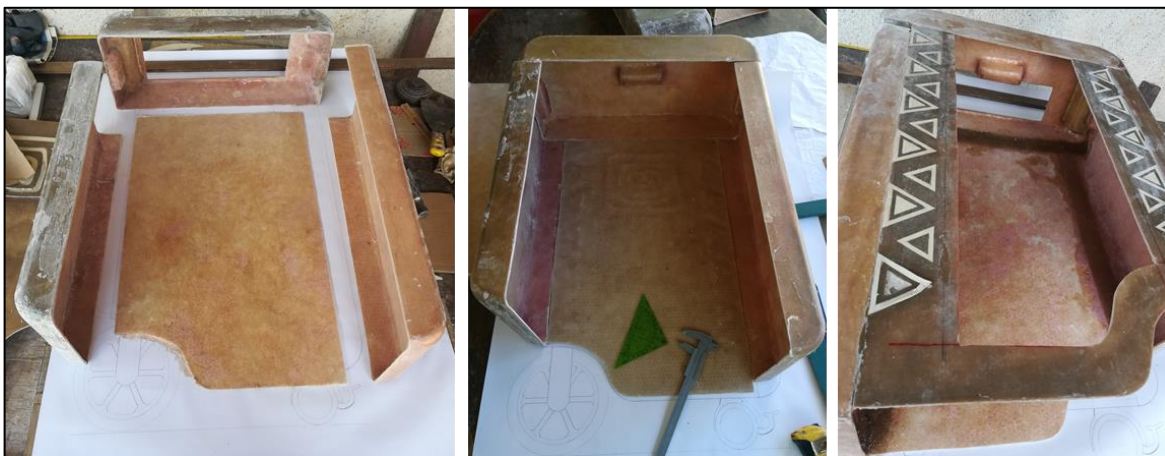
Soldadura de las partes que componen el casco del módulo 2.
